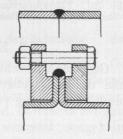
Abdichtung durch Verschweißen der Naht.
